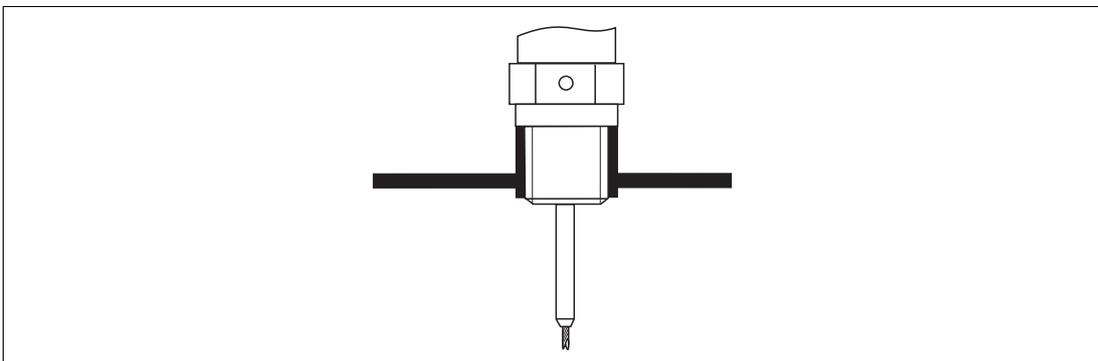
Montage mit Einschraubgewinde; bündig mit der Behälterdecke
